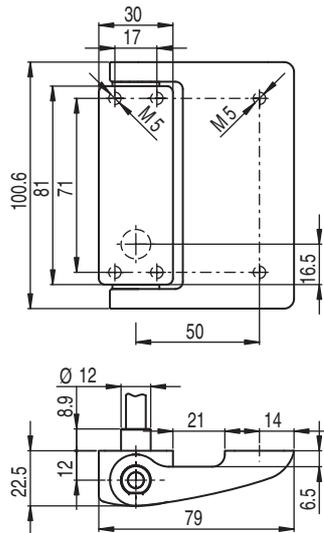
Dimensões do S410-M4-CB02M12-W e do S410-M4-CB2PUR-W em mm
